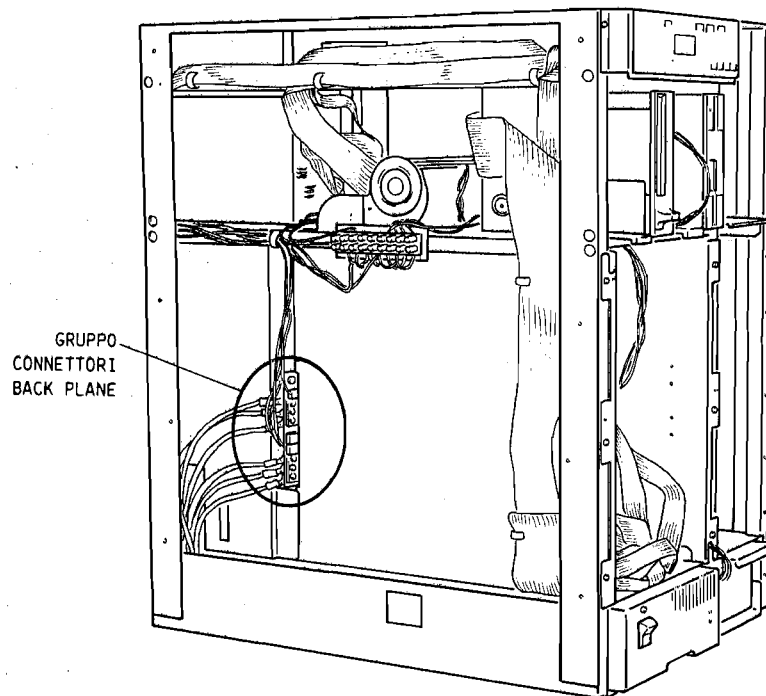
Posizione dei connettori del BACK PLANE riferita alla struttura del sistema
